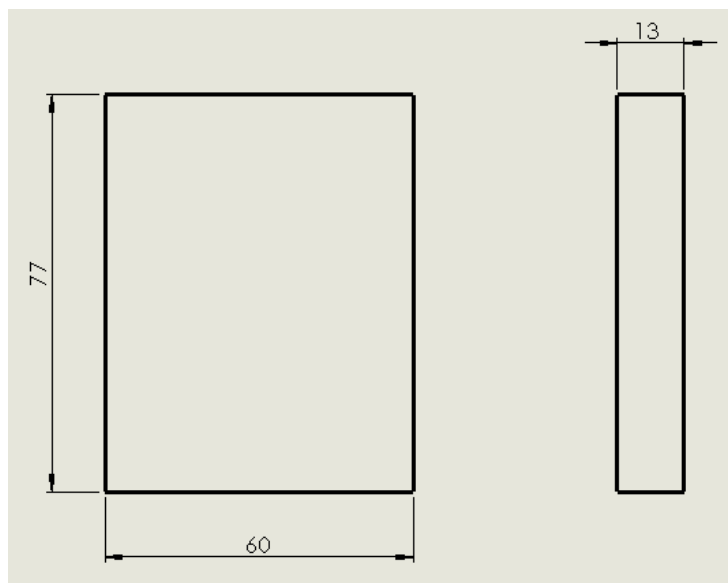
3. Placa de micro fundición de aluminio (mm).
